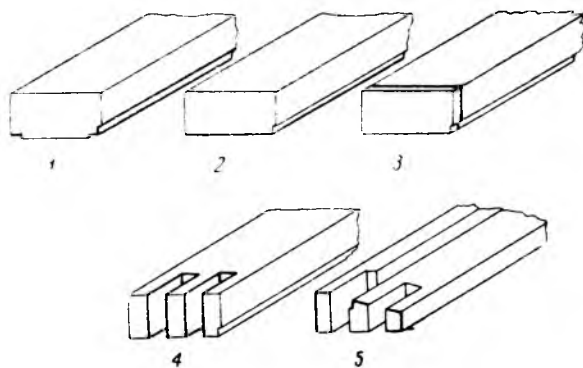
Схема обработки бруска на линии ДЛ8А:
